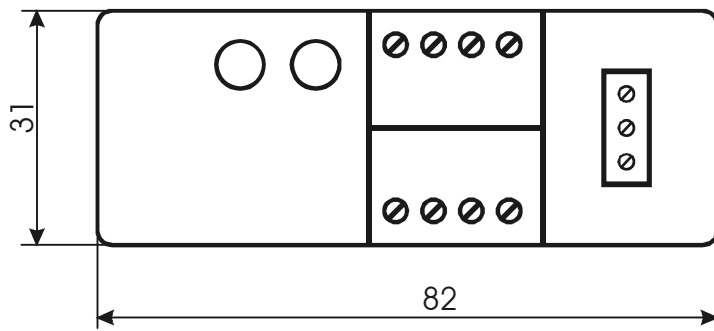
Габаритный чертеж ИП-40020-2-0
